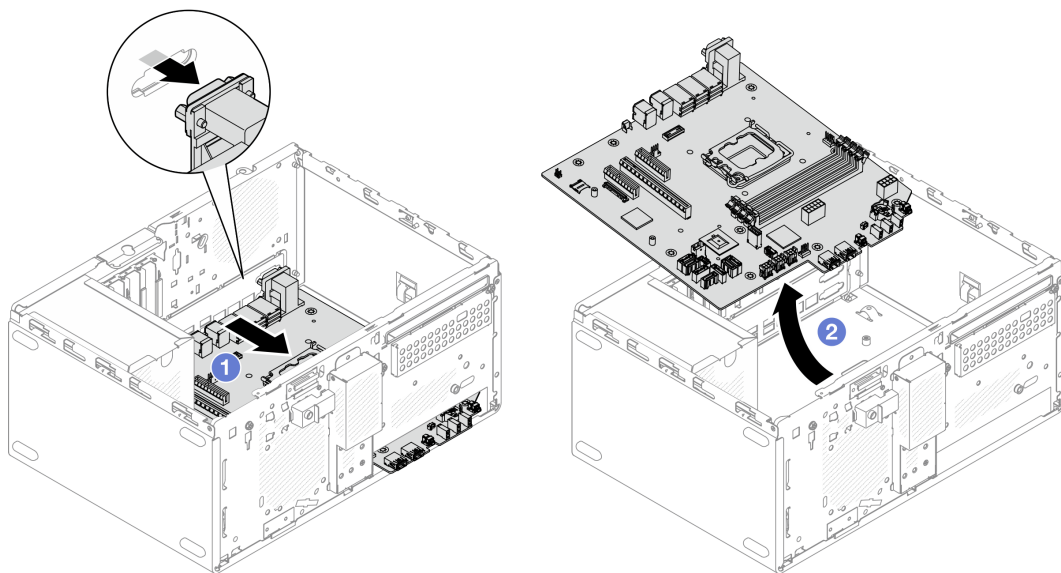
Entfernen der Systemplatine aus dem Gehäuse
